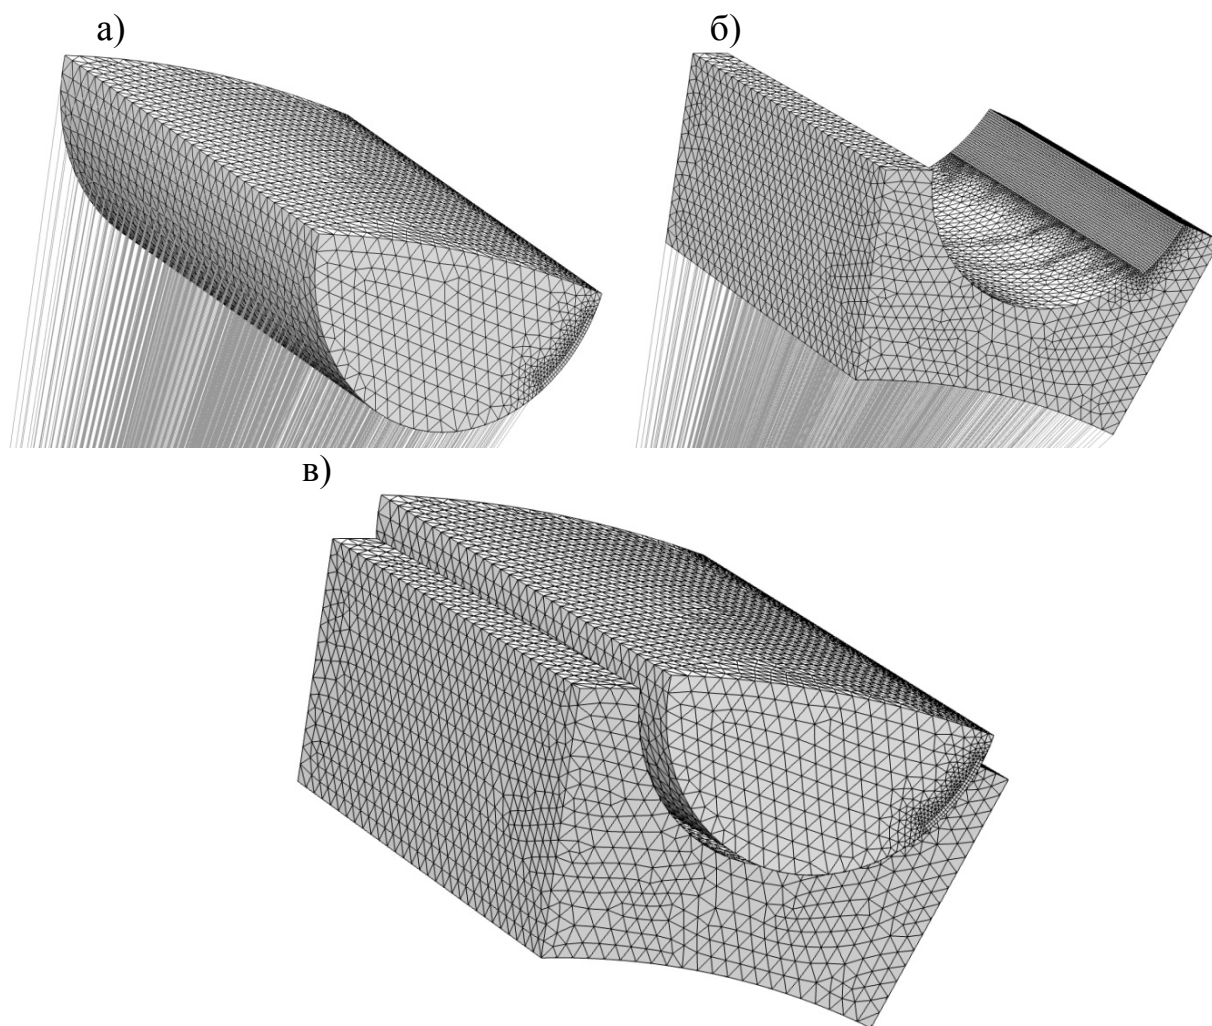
Конечно-элементная модель однопарного зацепления прецессионной передачи: а – зуб центрального колеса; б – зуб сателлита; в – зацепление
